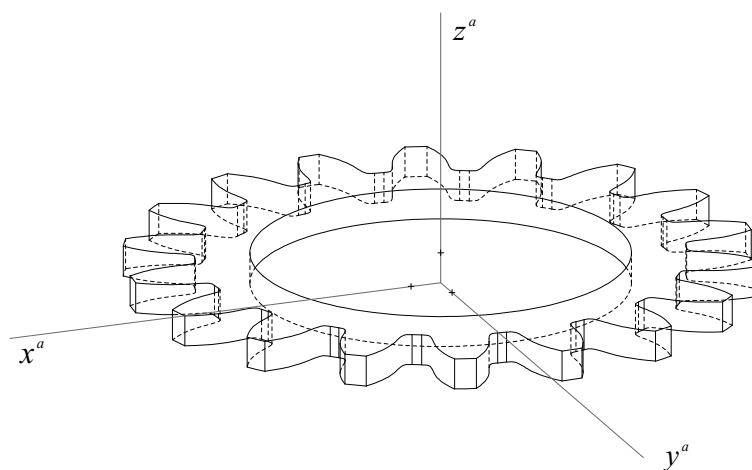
ozubené kolo v planometrii, 2. zadání
